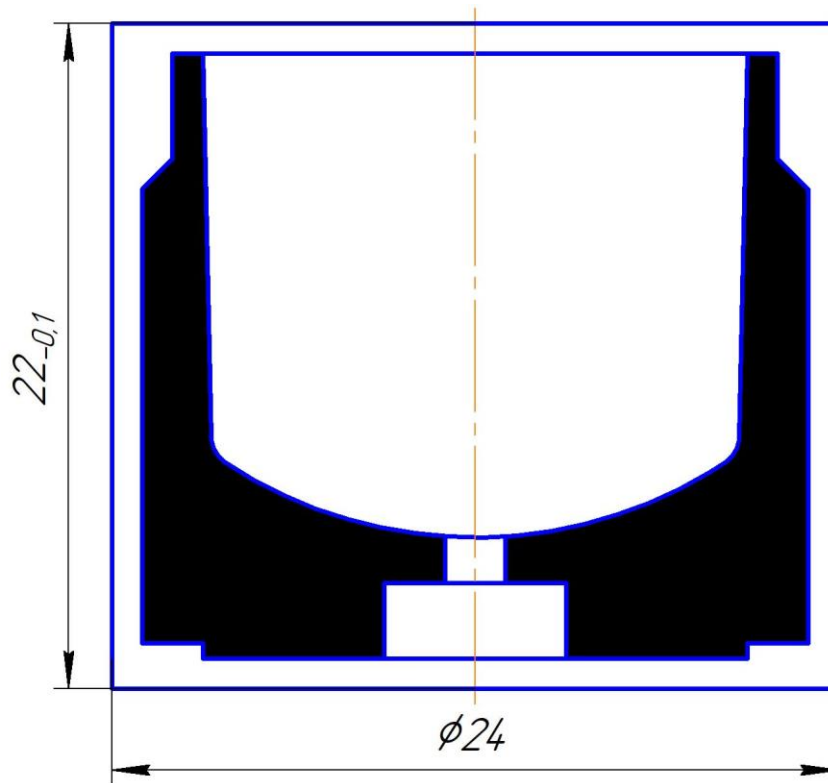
Заготовка деталі «Втулка» для механічної обробки.
